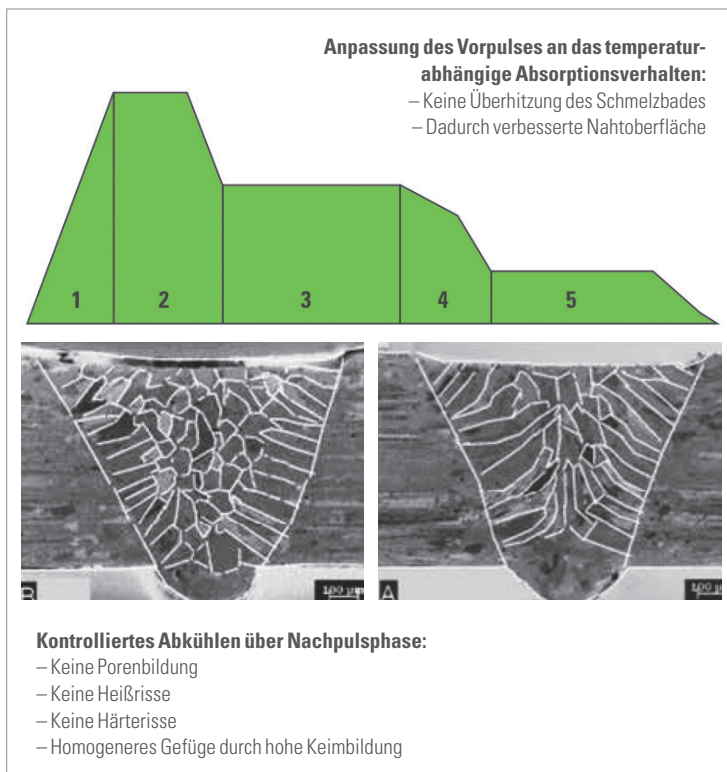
Pulsformung für bessere Schweißresultate.
